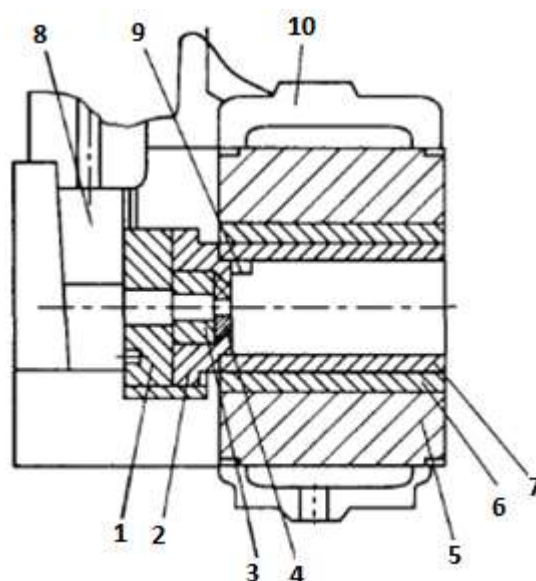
Конструкция контейнера: 1 – каретка; 2 – матрицедержатель; 3 – подкладное кольцо; 4 – матрица; 5 – наружная втулка; 6 – средняя втулка; 7 – рабочая втулка; 8 – конусное устройство для предотвращения осевого смещения; 9 – запор-фиксатор; 10 – подвижный траверс
